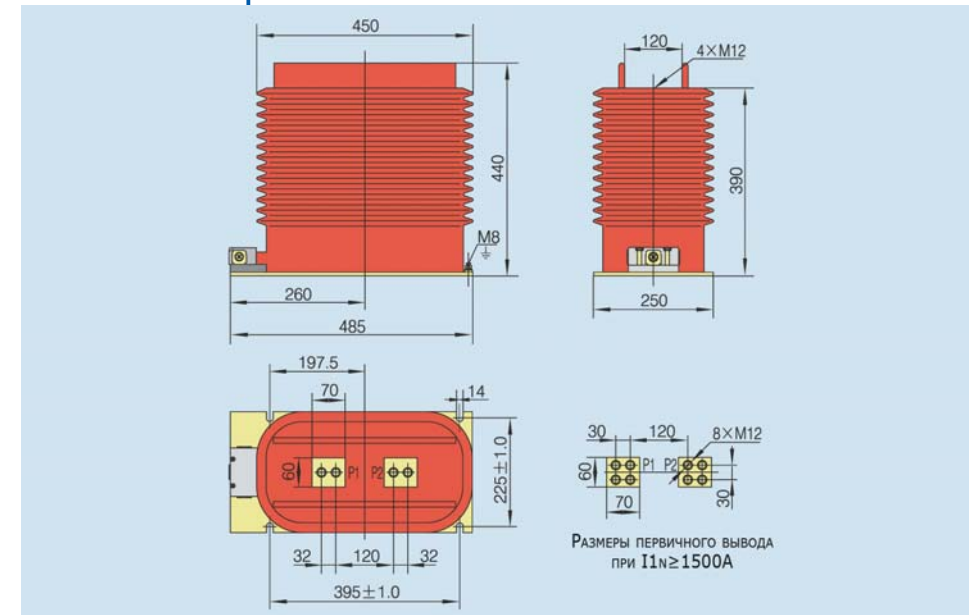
Внешний вид и размеры трансформатора тока LZZB8-35A
